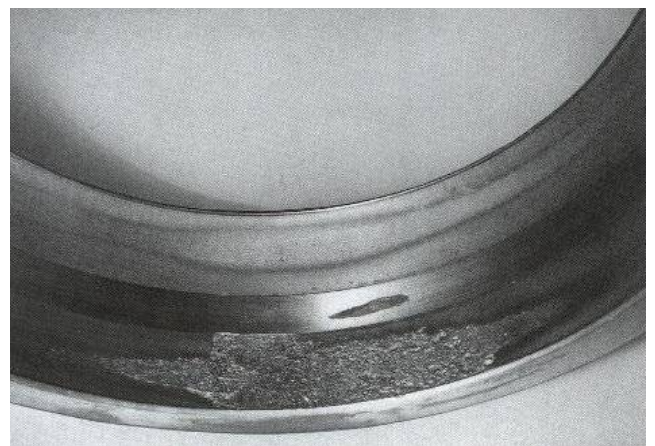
Defecto en la pista exterior de un rodamiento
